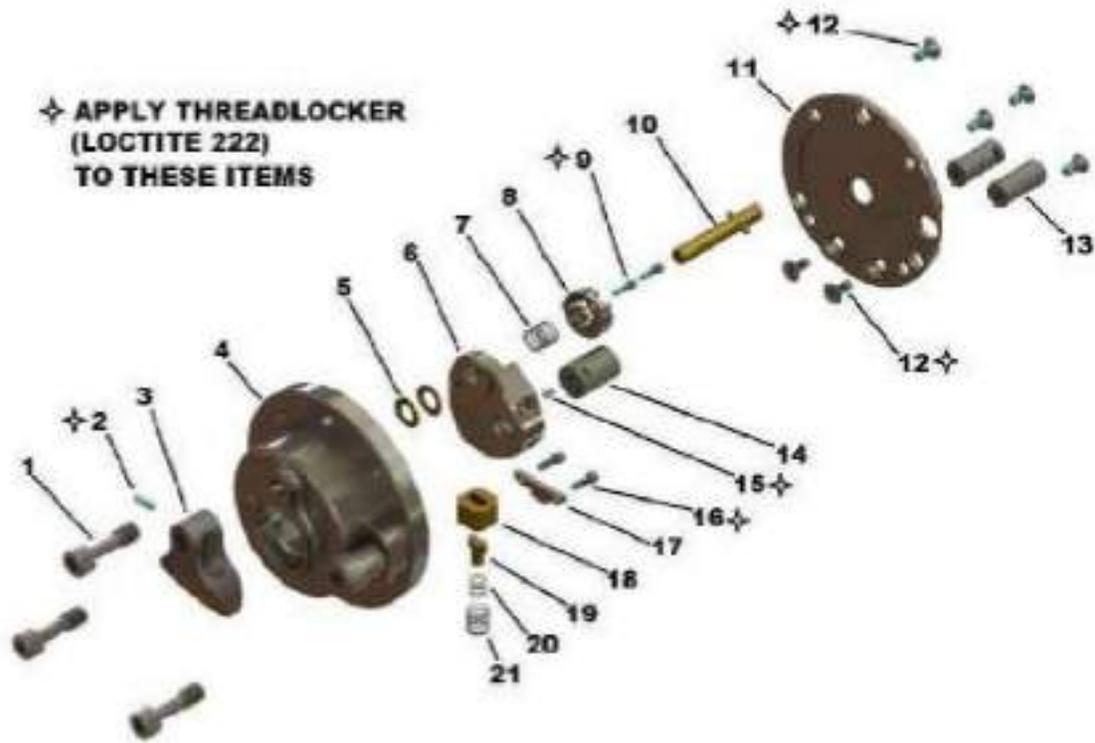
Vue éclatée des composants de l'assemblage de la plaque avant
